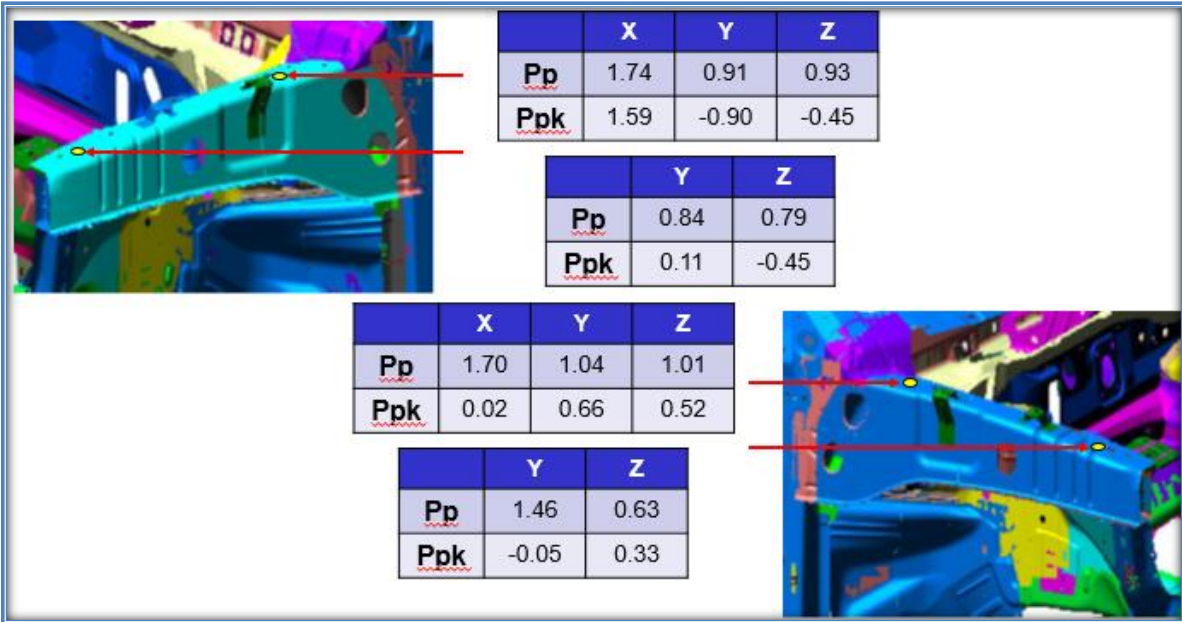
Dimensiones de las Escopetas del Compartimiento del Motor Explorer. Fuente: Imagen suministrada por CMM.
